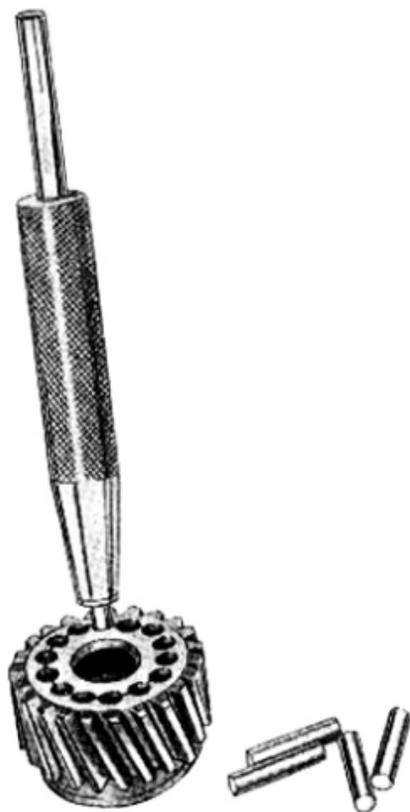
Come viene operato il montaggio dei cilindretti nel pignone motore
